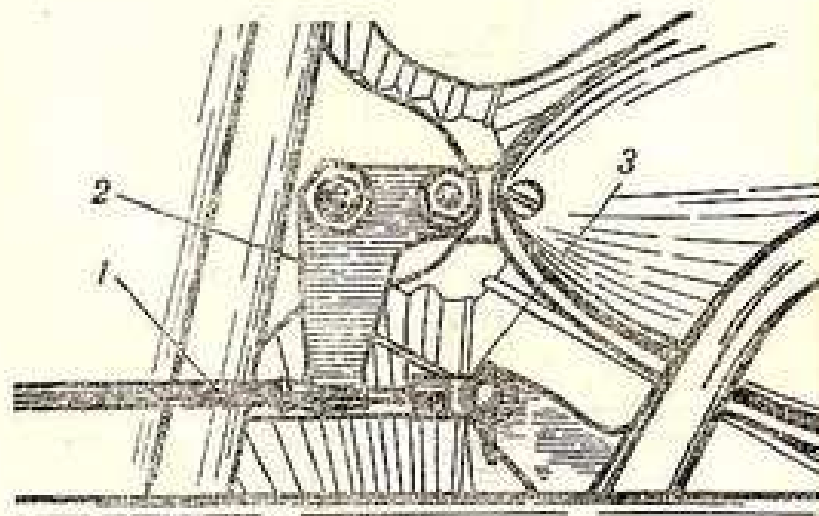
УСТАНОВКА ТРОСА ТОРМОЗА:
